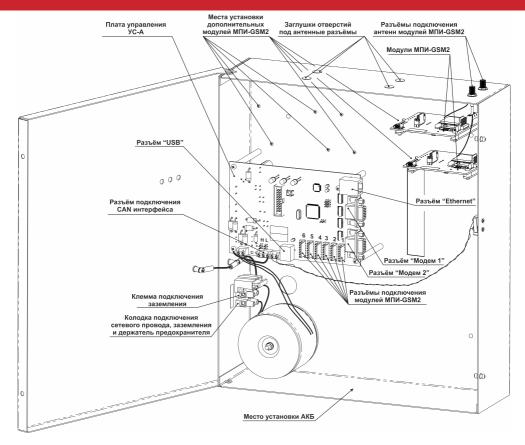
Вид устройства УС-А с открытой крышкой
